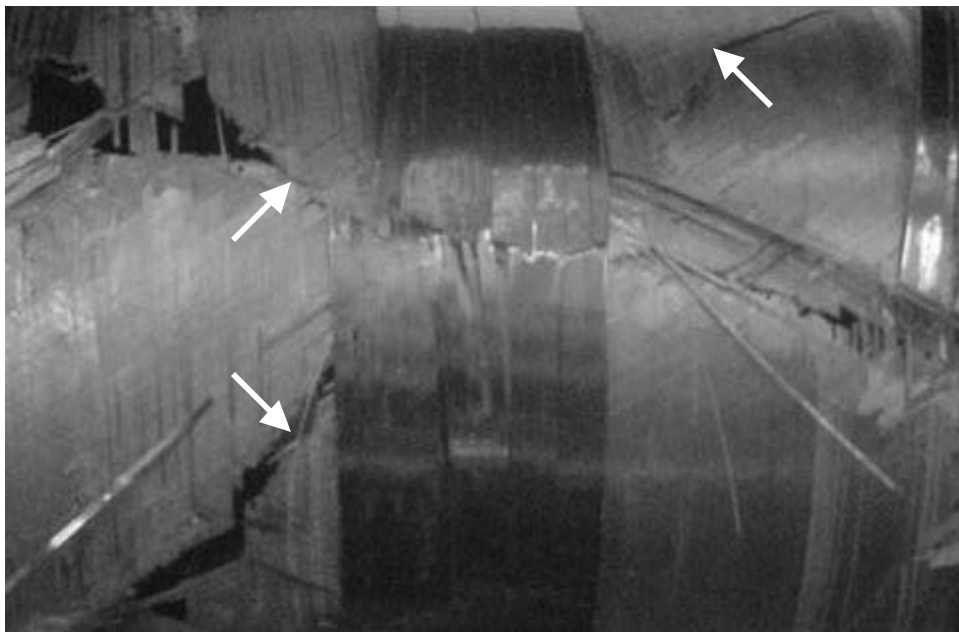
Aspecto final de um cilindro com bobinagem assimétrica após ensaio hidrostático.
